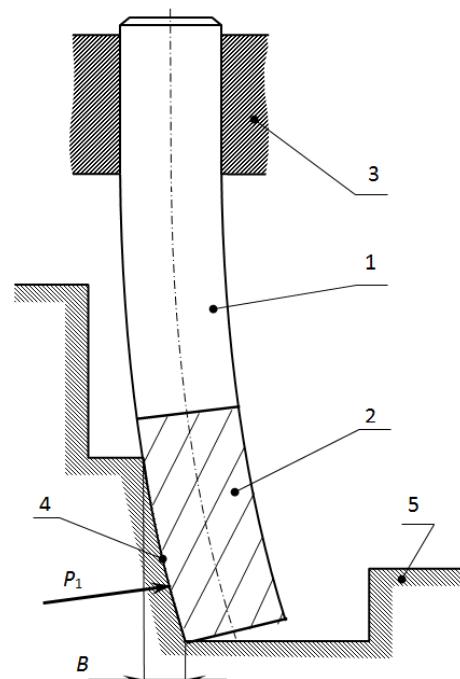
Схема образования отклонения B от вертикали положения стенки обрабатываемого паза при действии радиальной составляющей P_1 силы резания: 1 – хвостовик фрезы; 2 – твердосплавная режущая часть фрезы; 3 – зажимное устройство станка; 4 – обработанная поверхность паза заготовки; 5 –
